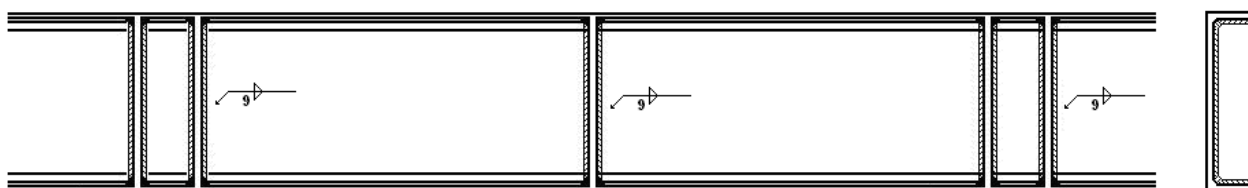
Soldadura dos reforços nas secções de apoio dos actuadores e secção central da viga
